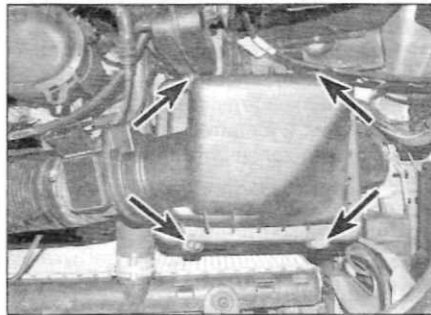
Выверните четыре винта (отмечены стрелками) крепления крышки к корпусу воздушного фильтра (поздние модели с двигателем 1.9 л)
